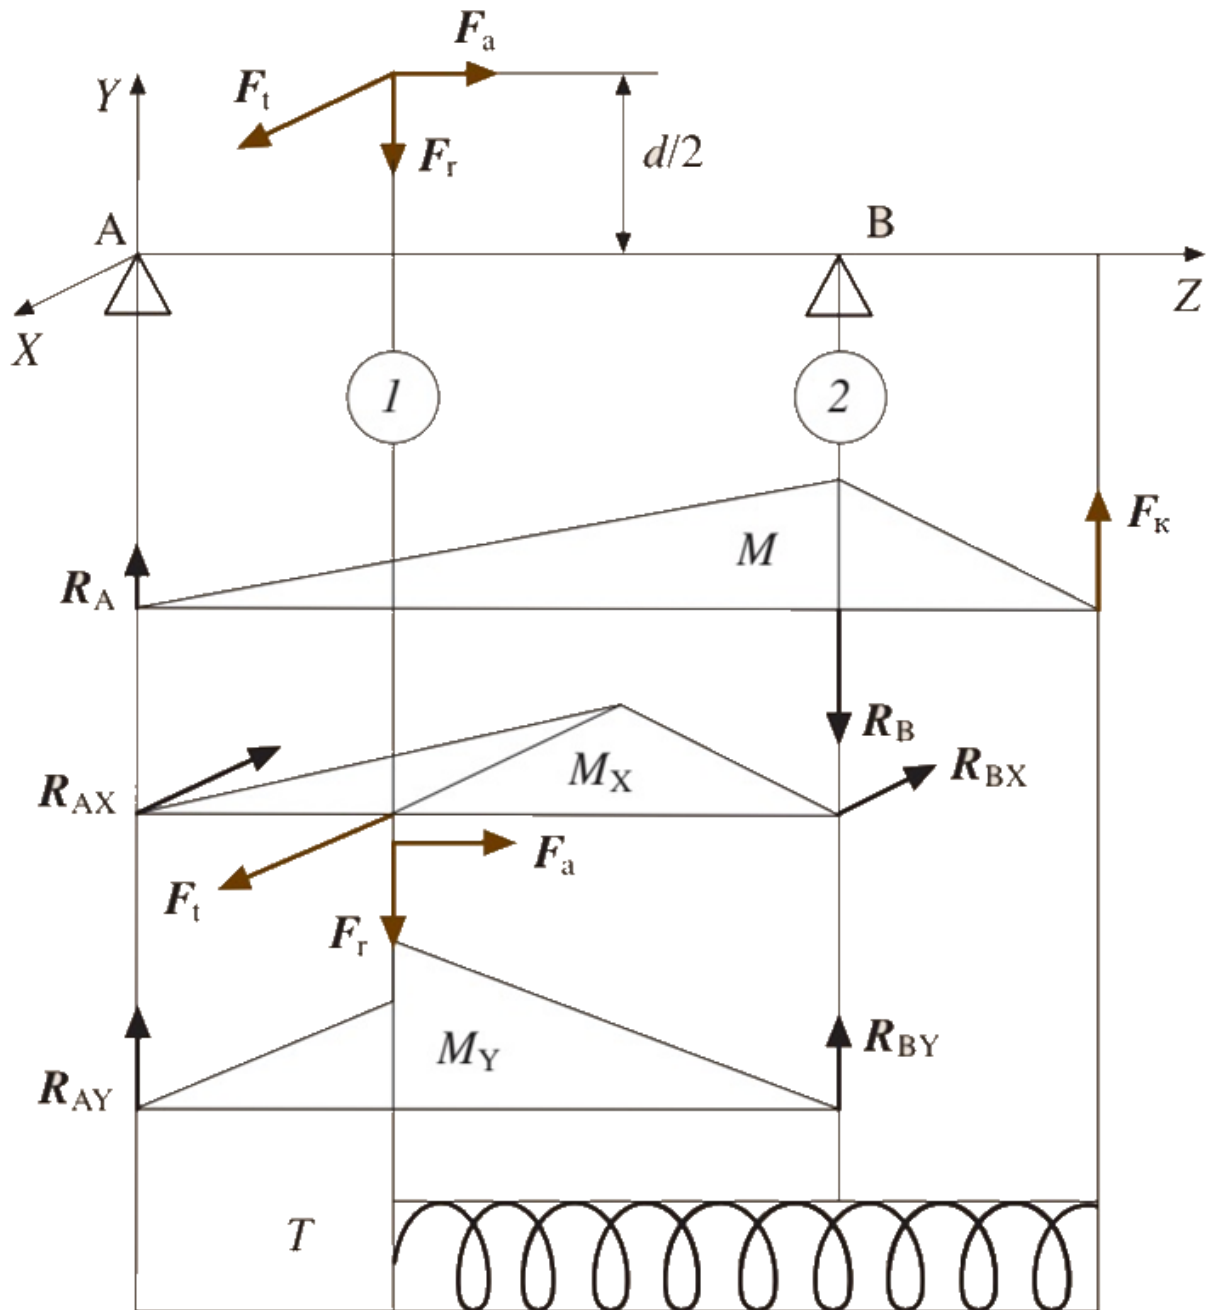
Вихідний вал двоступеневого циліндричного редуктора
